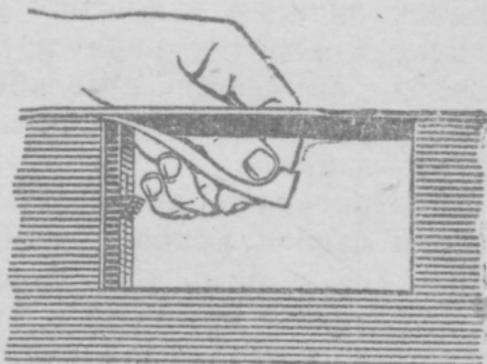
Проверка прилегания боевой личинки к крышке короба
